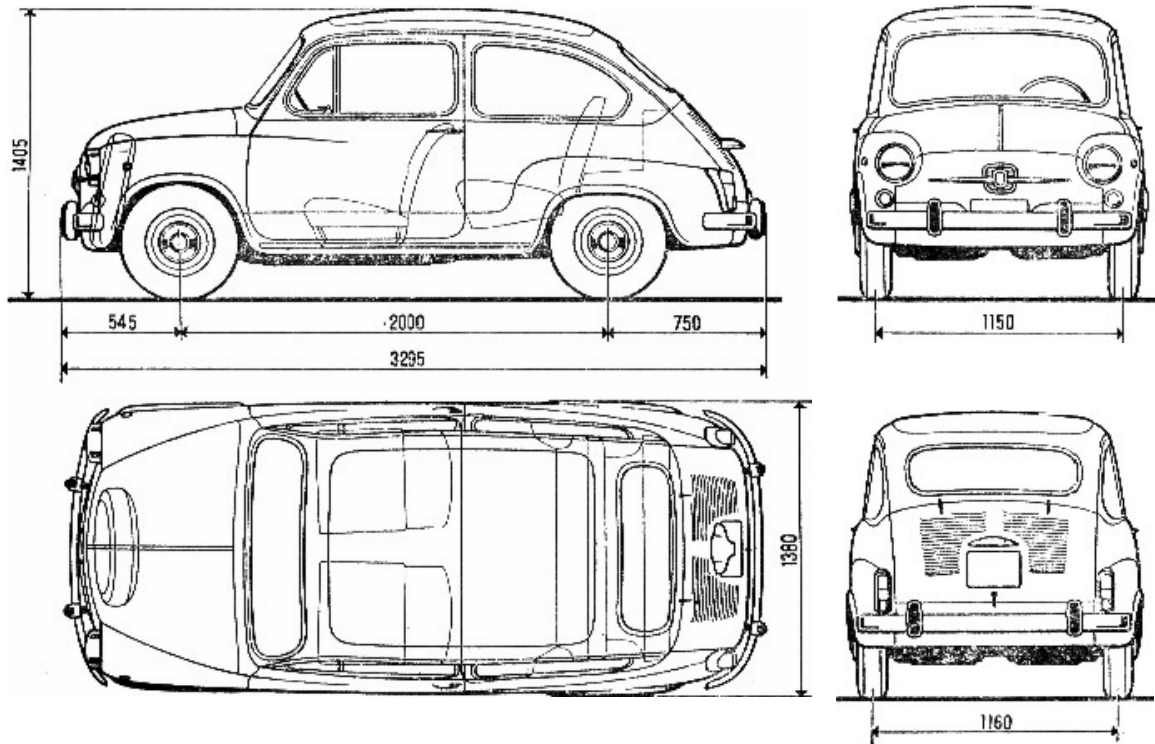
Dimensiones del Fiat 600-D y E.
